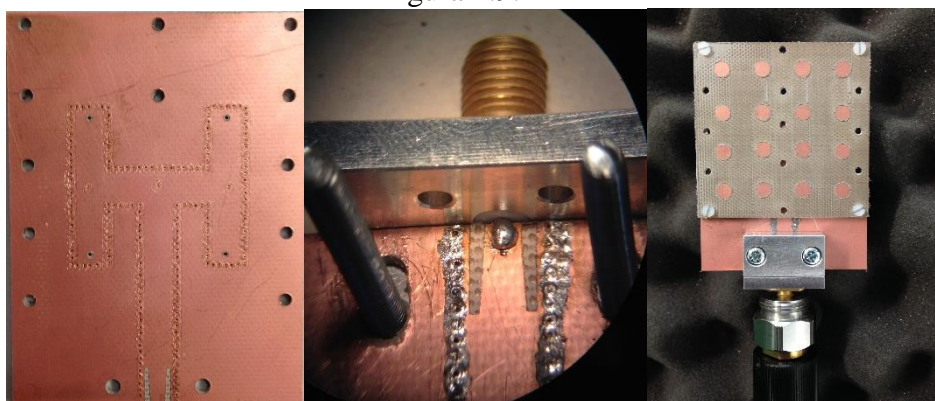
Nueva red SIW construida (izda), vista del conector SMA soldado (centro) y antena montada y lista para ser medida en adaptación (dcha).
